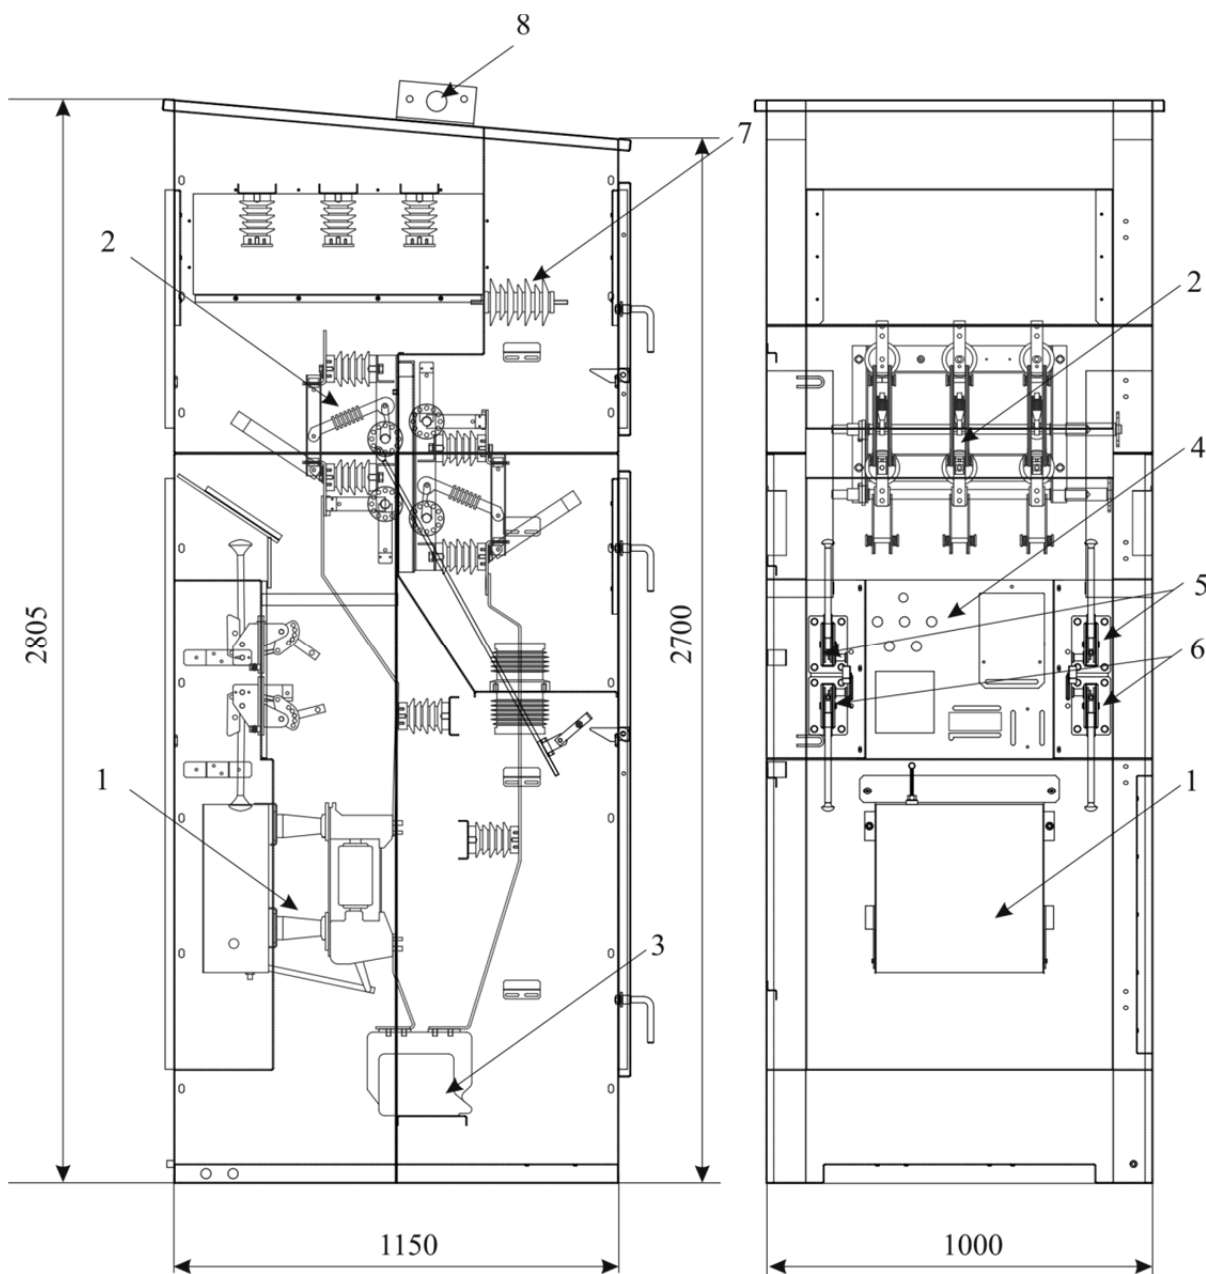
Габаритные размеры и устройство КРН с вакуумным выключателем
